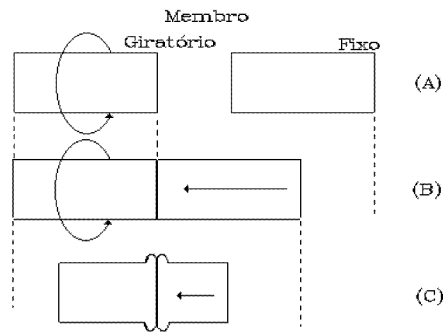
Etapas da Soldagem por Fricção Inercial.
